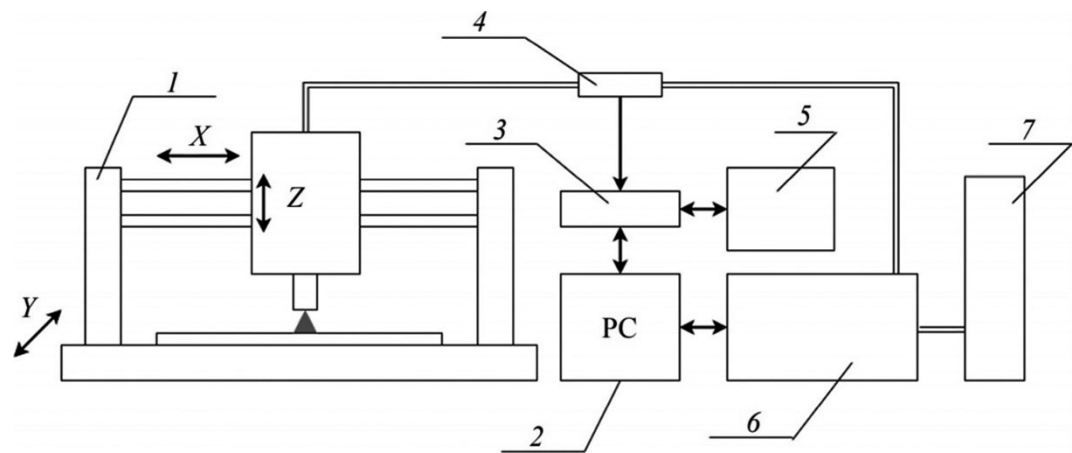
Схема экспериментального стенда WAAM на базе станка с ЧПУ: 1 — трехкоординатный станок с ЧПУ портального типа; 2 — ПК; 3 — АЦП/ЦАП; 4 — датчики силы тока и напряжения; 5 — система ЧПУ; 6 — сварочный полуавтомат; 7 — баллоны с защитным газом
